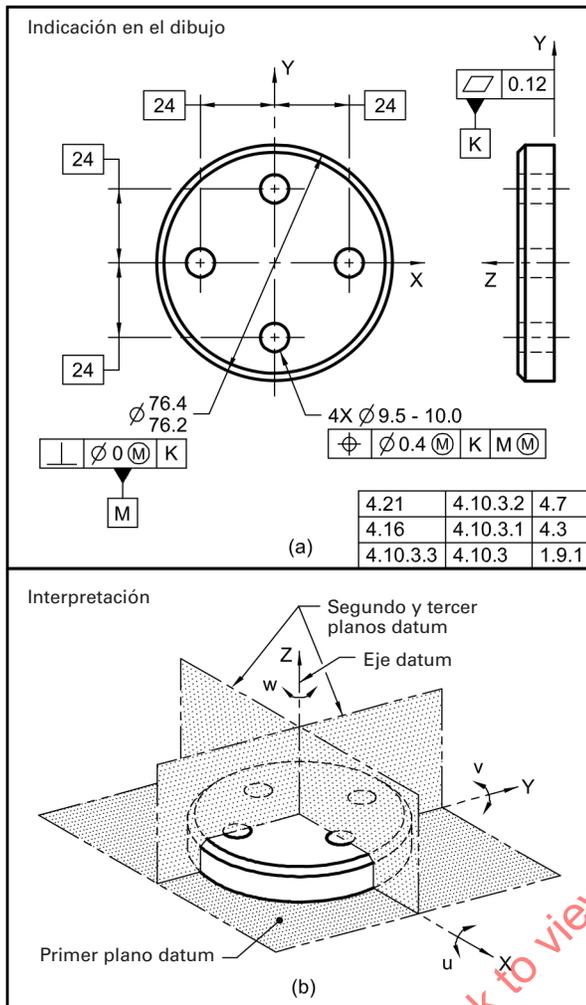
Pieza con Elemento Datum Cilíndrico
